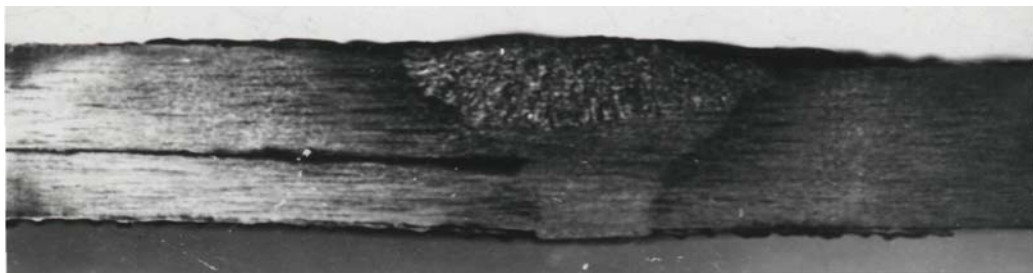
Расслоение стенки трубы у кольцевого сварного шва
